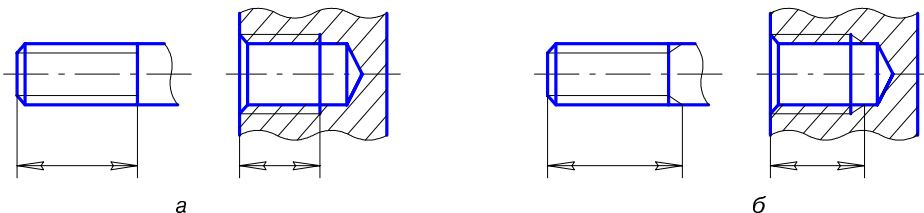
Размер длины резьбы: а — с полным профилем; б — со сбегом
